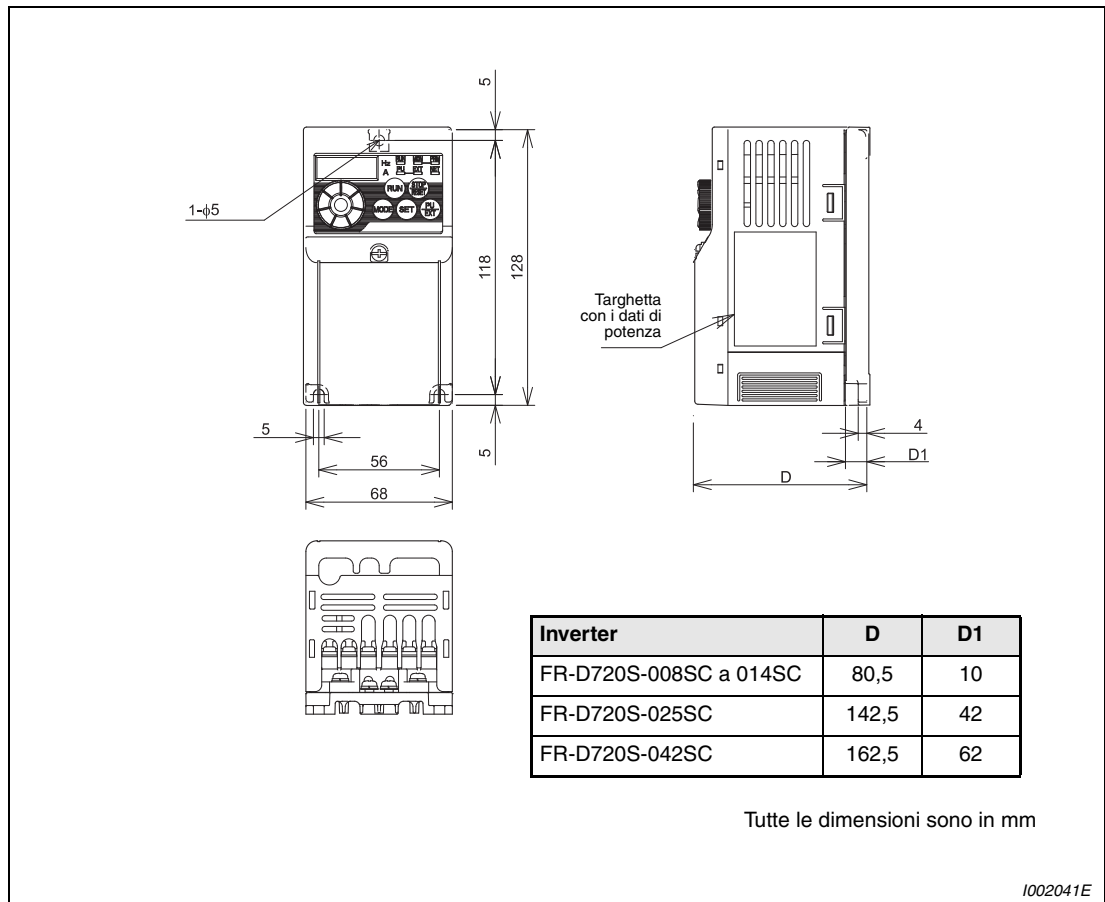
Dimensioni degli inverter da FR-D720S-008SC a 042SC
